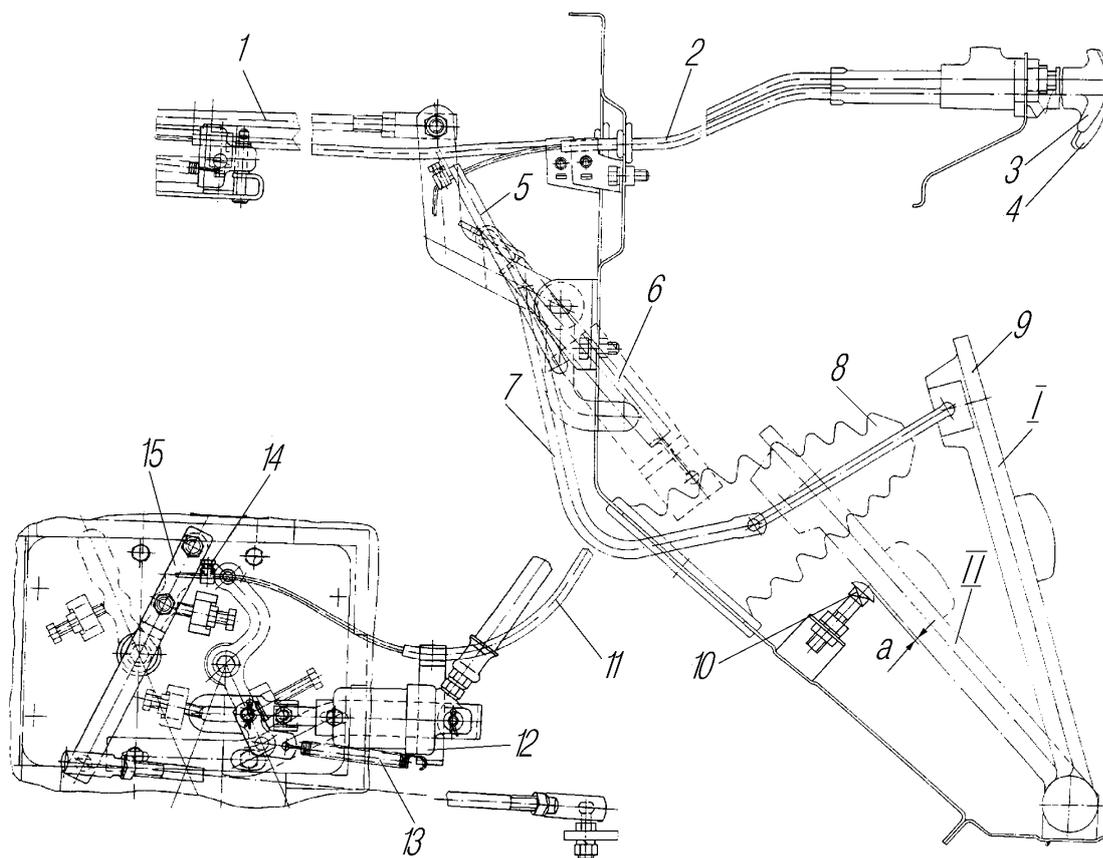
Привод управления подачей топлива и ручного останова двигателя:
